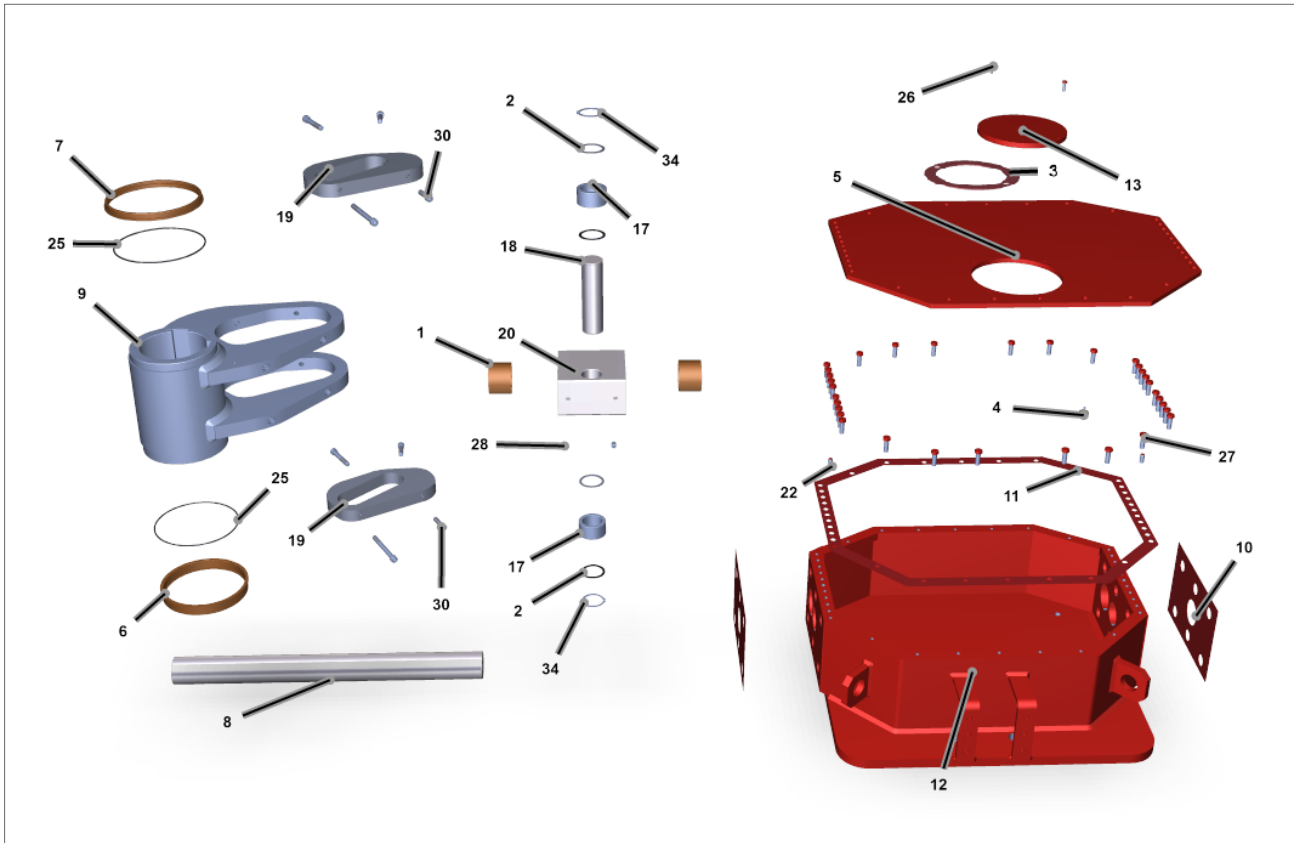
Mittelkörper (geschweißt) (Größe Stellantrieb 200, 201, 270, 271)
